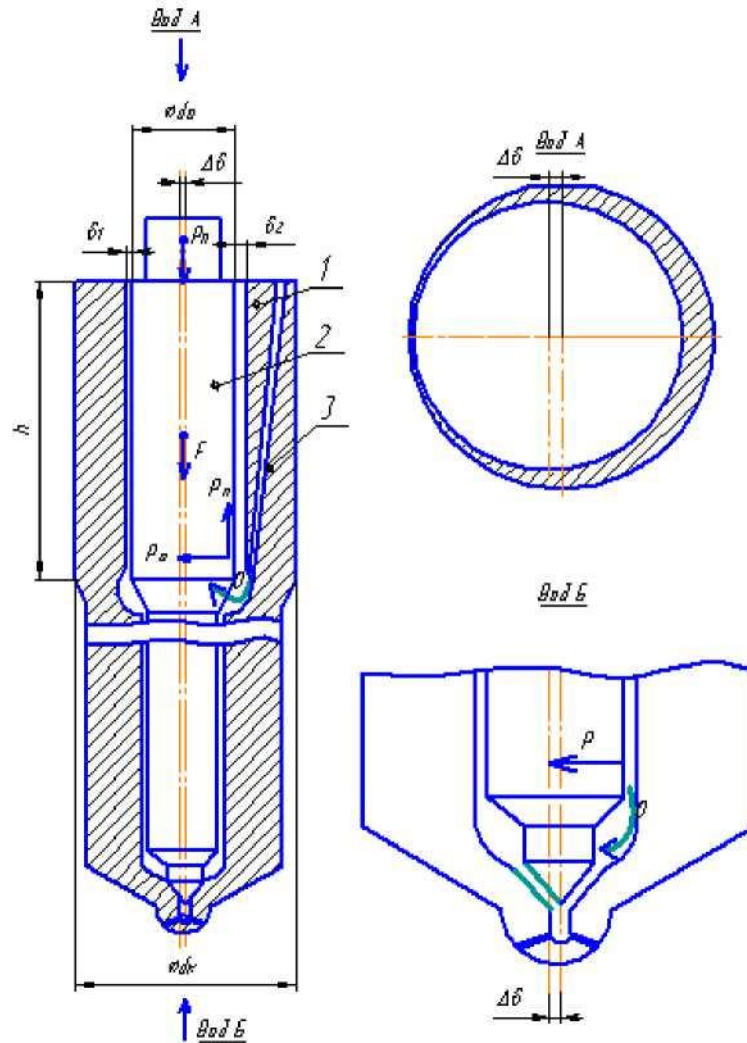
Схема сил, що діють на розпилювальний елемент форсунки дизельної форсунки: 1 - корпус, 2 - голка, 3 - канал подачі палива.
